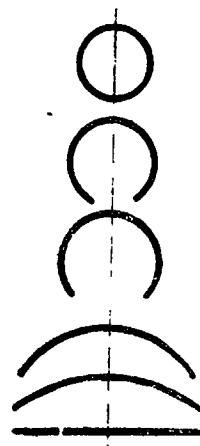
Последовательное изменение заготовки в валках электросварочного стана
